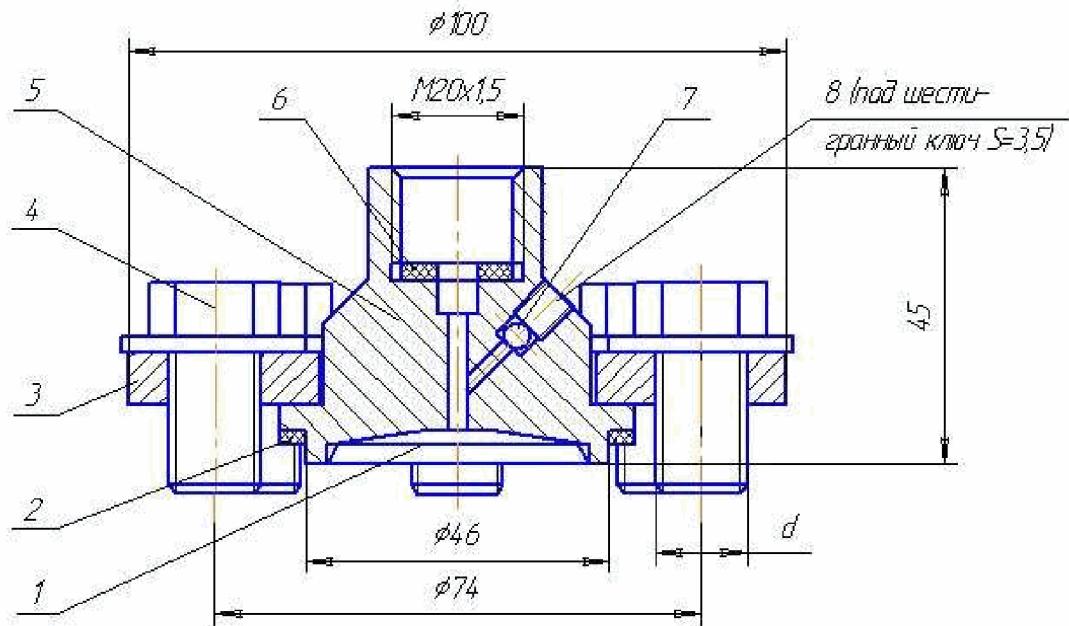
Конструкция, габаритные и присоединительные размеры
